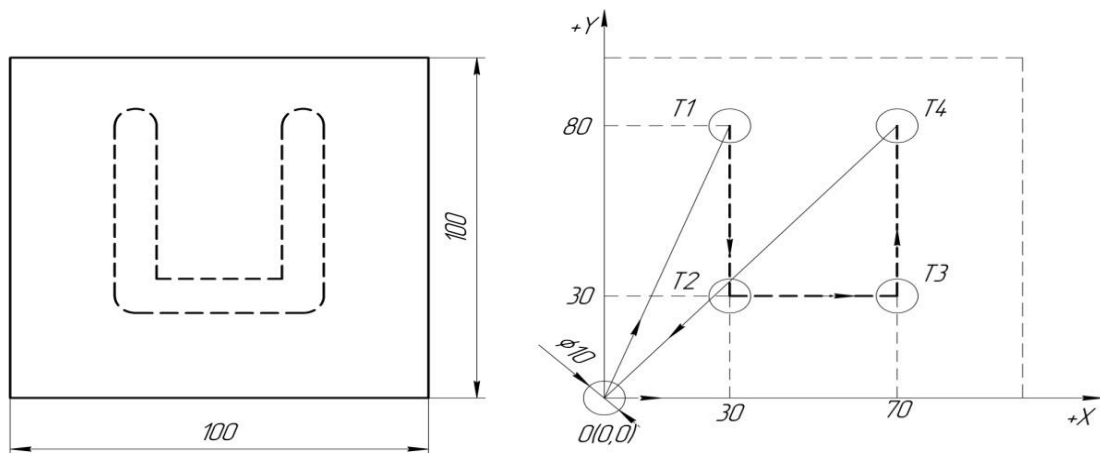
Ескіз заготовки та розташування її в прямокутній системі координат
